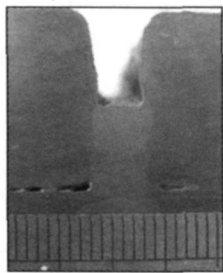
焊剂带约束电弧超窄间隙焊缝截面
